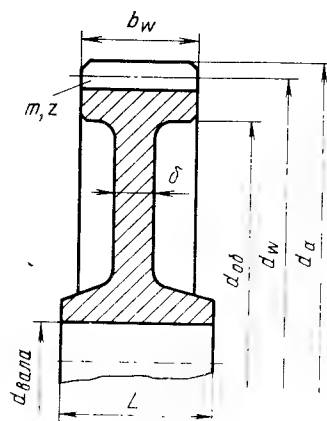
Зубчатое колесо цилиндрической передачи
